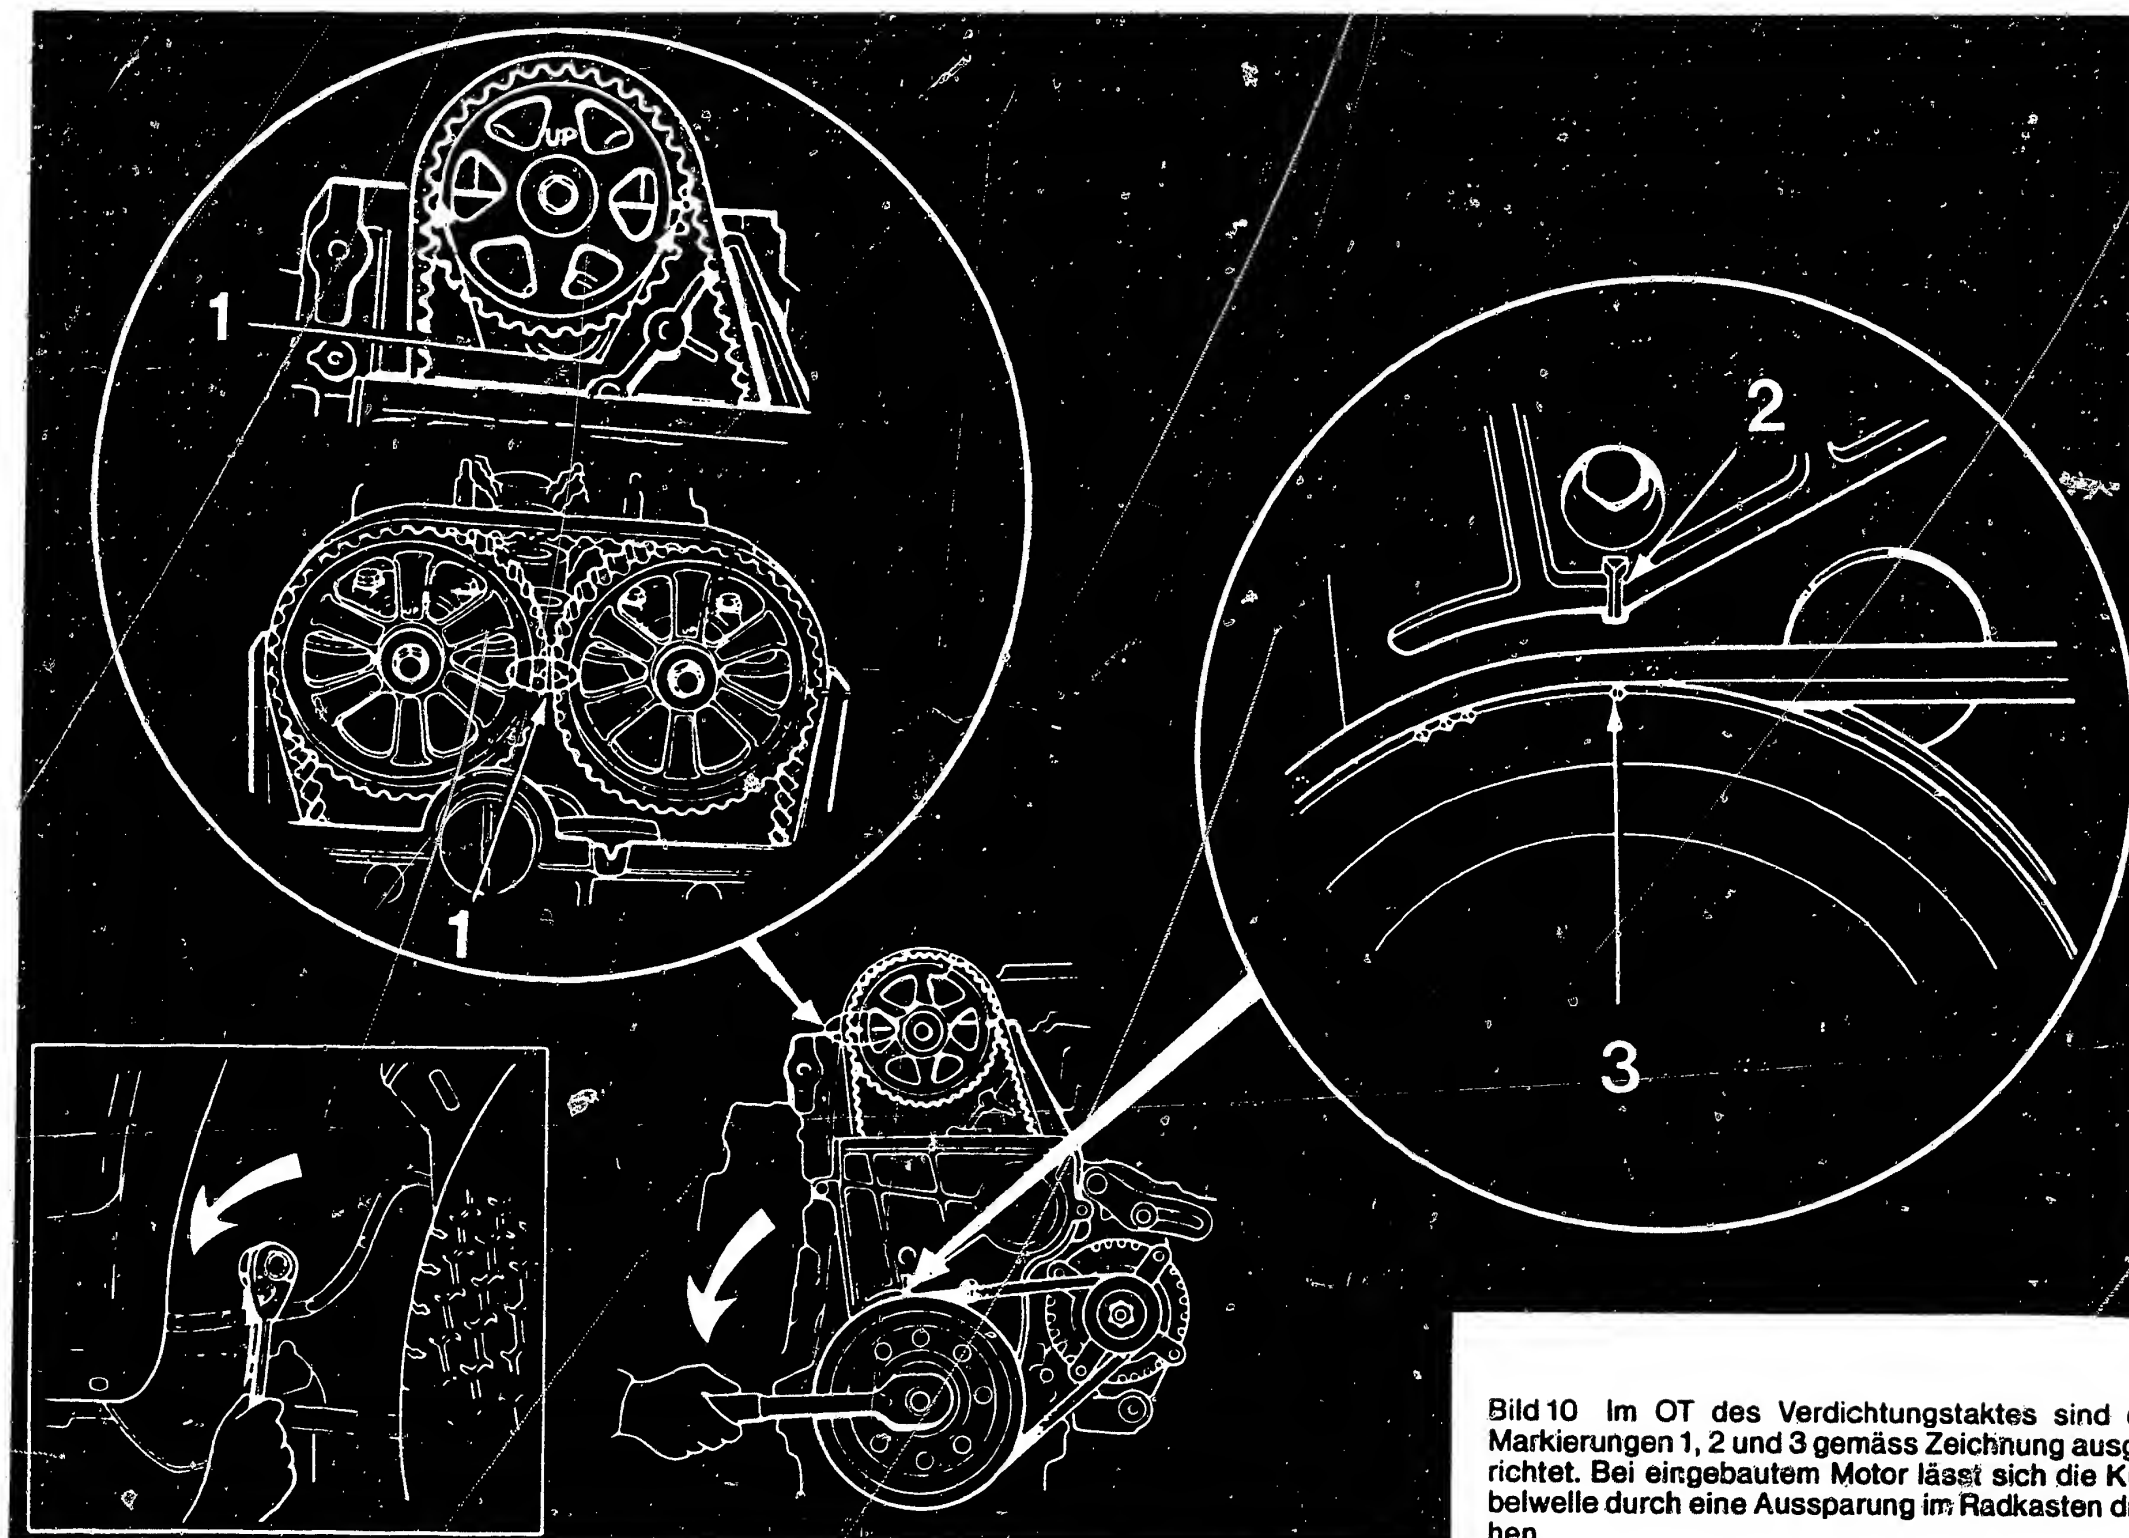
Im OT des Verdichtungsaktes sind die Markierungen 1, 2 und 3 gemäss Zeichnung ausgerichtet. Bei eingebautem Motor lässt sich die Kurbelwelle durch eine Aussparung im Radkasten drehen.
